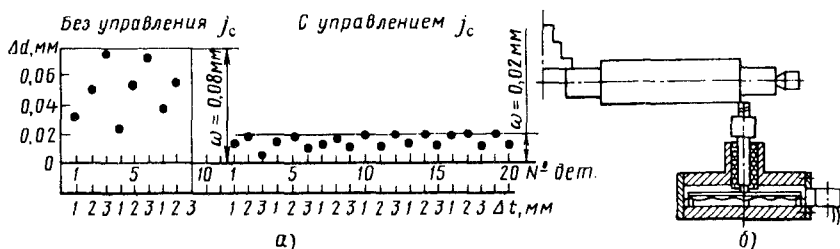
Обработка валиков на токарно-винторезном станке:
